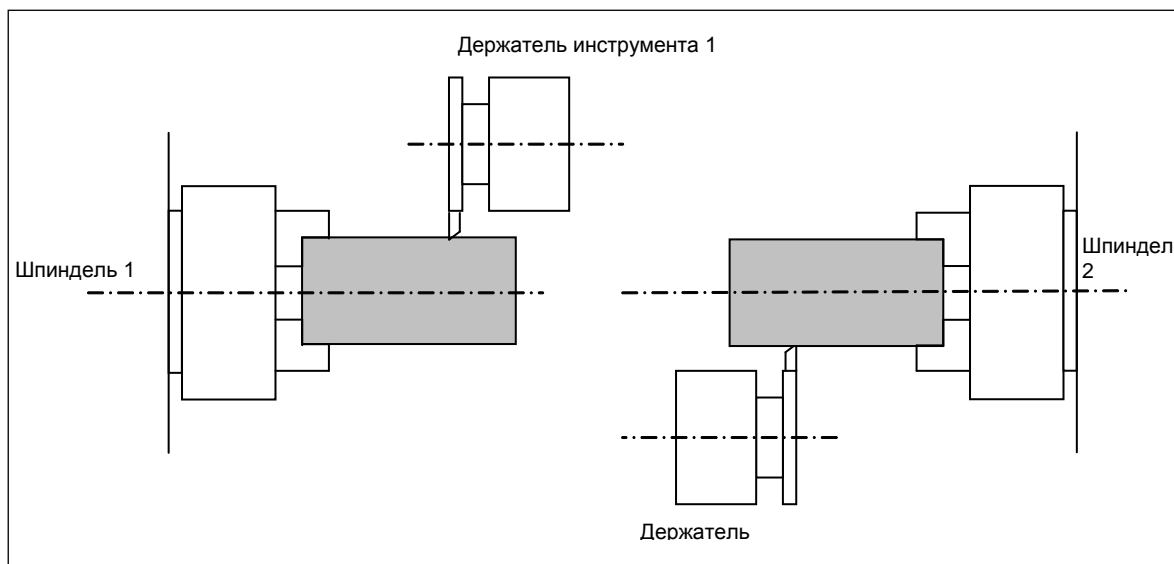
(b) Применение на станке с двумя шпинделями и двумя резцедержателями
